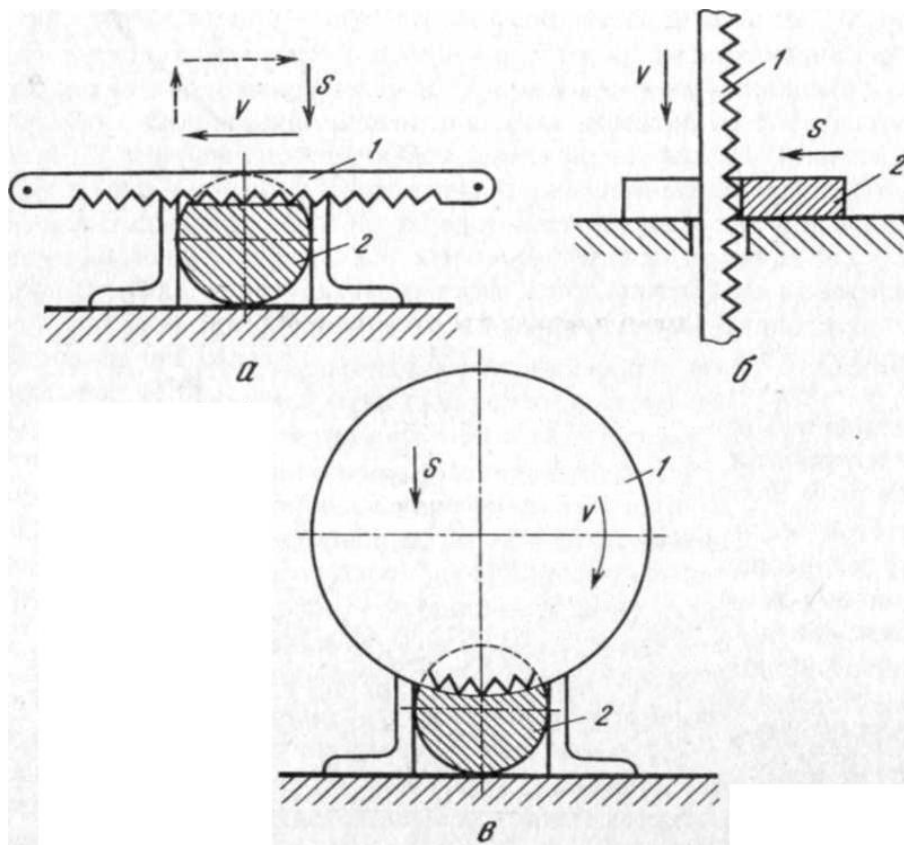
Схема обработки заготовок на отрезных станках: 1 – инструмент, 2 – заготовка.
